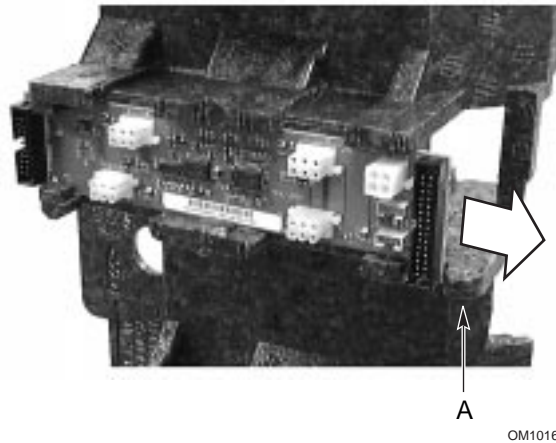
Removendo e instalando a placa de distribuição do ventilador
